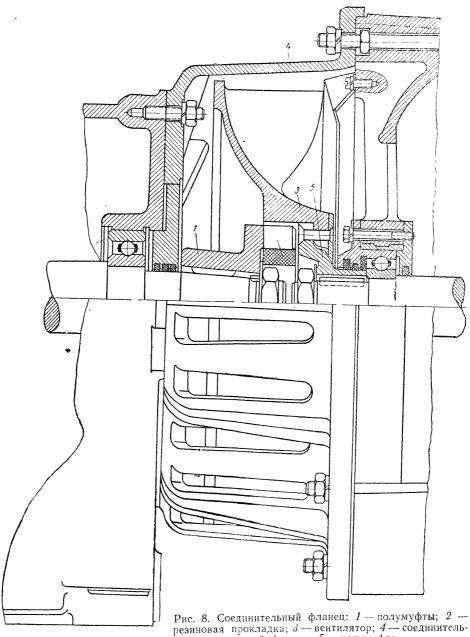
Соединительный фланец: I — полумуфты; 2 — резиновая прокладка; δ — вентилятор; 4 — соединительный фланец; δ — полумуфта
